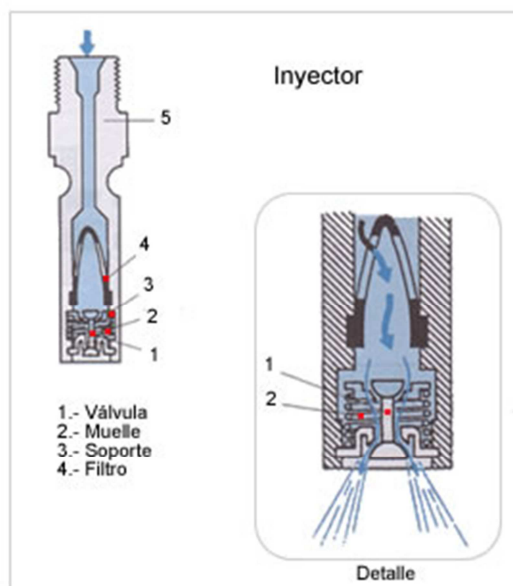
Partes internas del inyector de Combustible (Sistema K-Jetronic)
